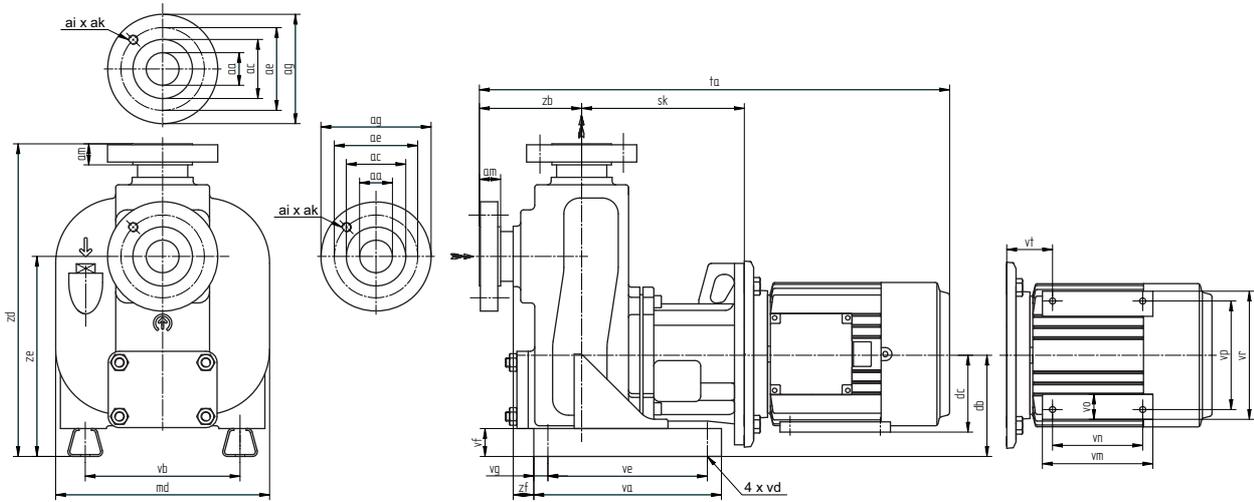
FRES mit ISO 7005 PN20 Anschlüssen.
